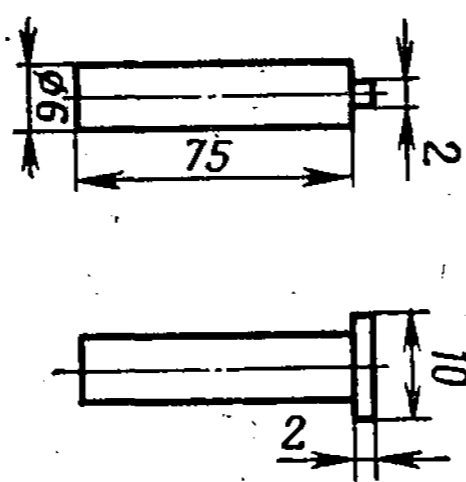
Палец для замены верхних вкладышей коренных подшипников
